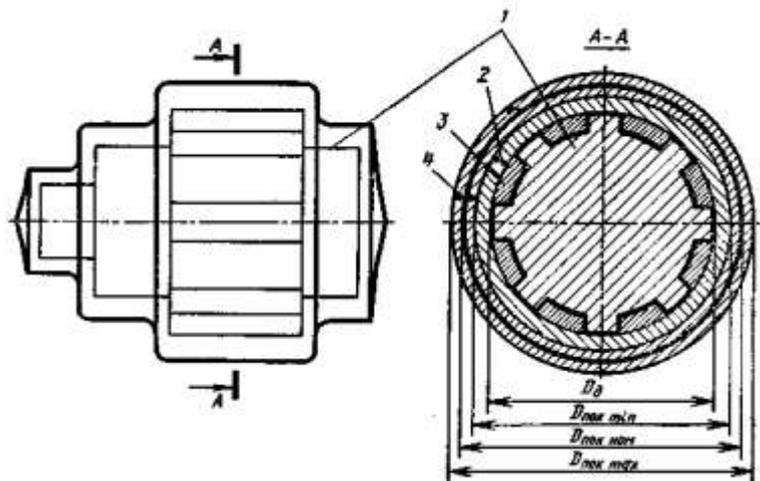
Схема размеров поковки с напуском, припуском и допуском
